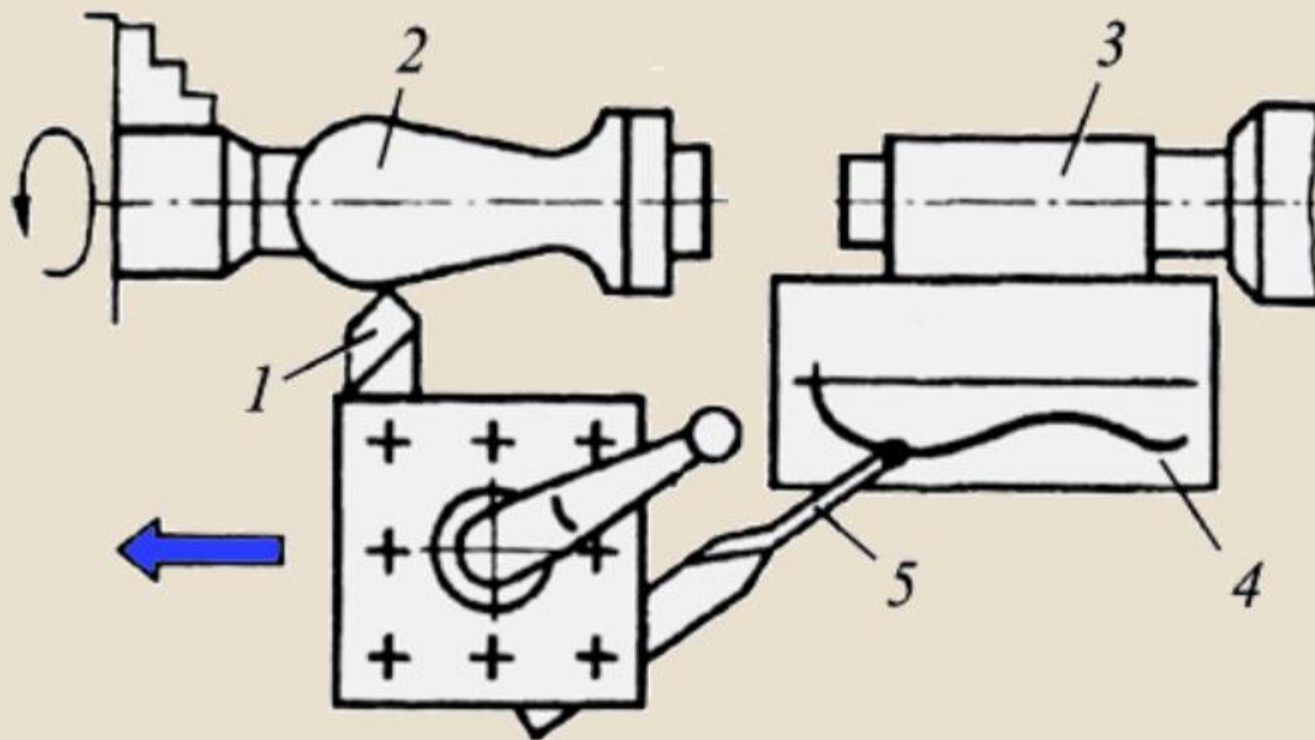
Оброблення фасонних поверхонь способом поєднання двох подач з контролем за кресленням:
